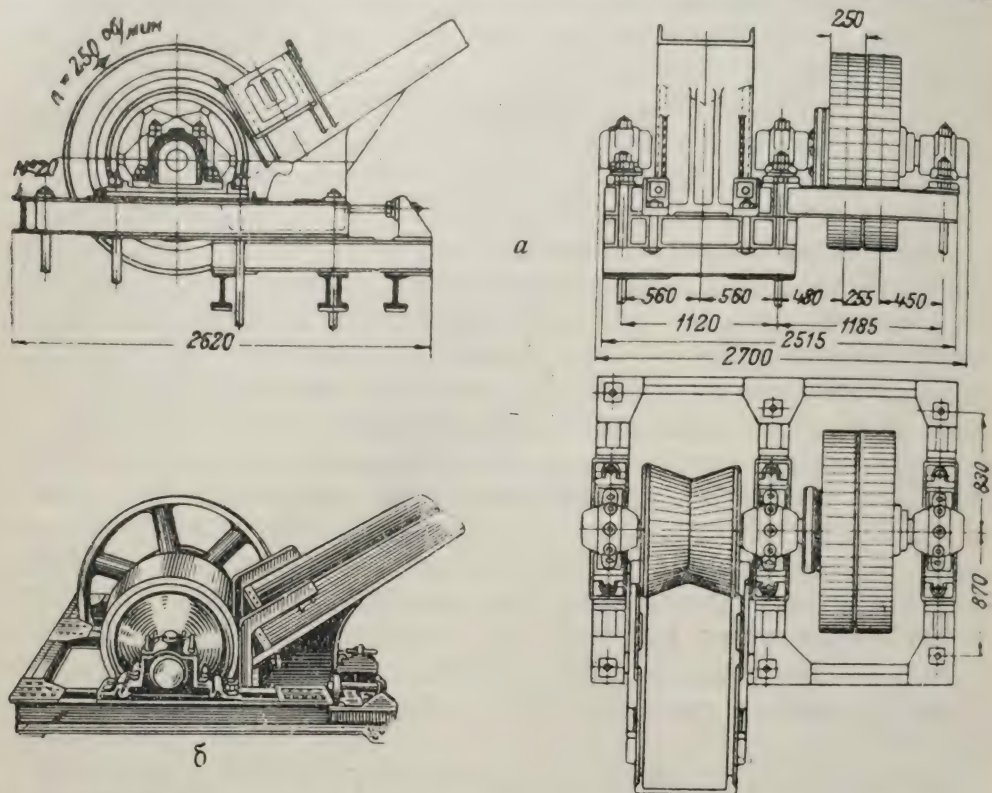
Рубильный станок для измельчения дубовой древесины (РСА):
